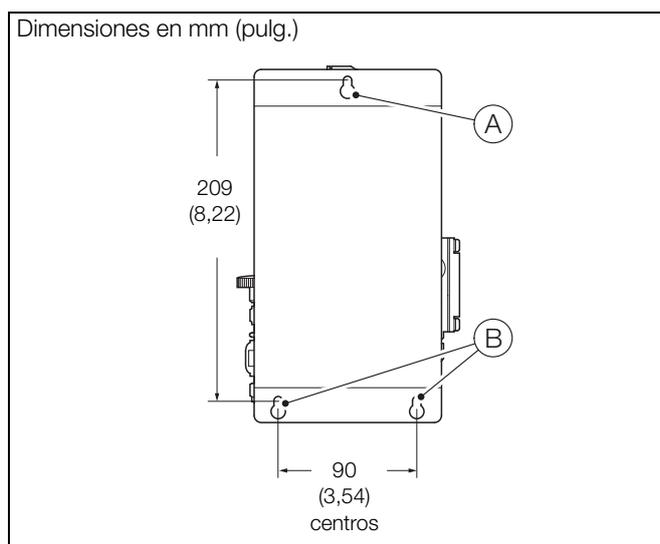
Montaje del panel de la sección de medición ADS551
